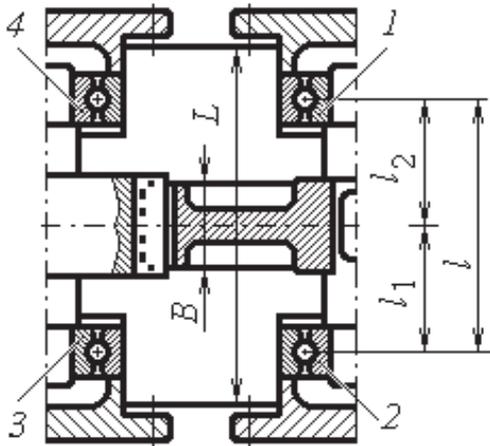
Конструкция цилиндрической зубчатой передачи коробки отбора мощности грузового автомобиля: 1, 2, 3, 4 - номера опор корпуса
